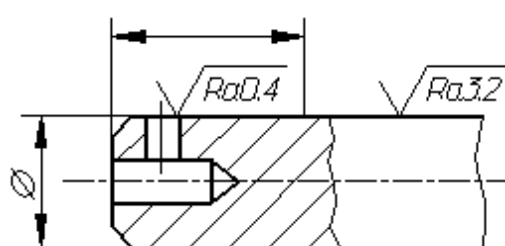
Пример обозначения различной шероховатости на одной поверхности
